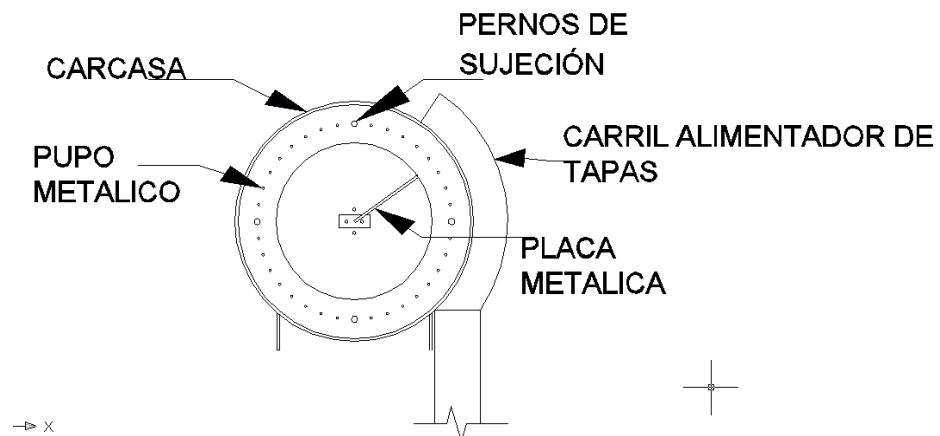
PARTES DE TAMBOR ROTATORIO.
